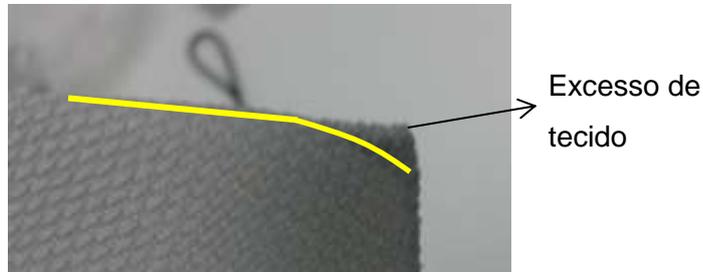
Retrabalho de soldadura na zona superior da peça.
